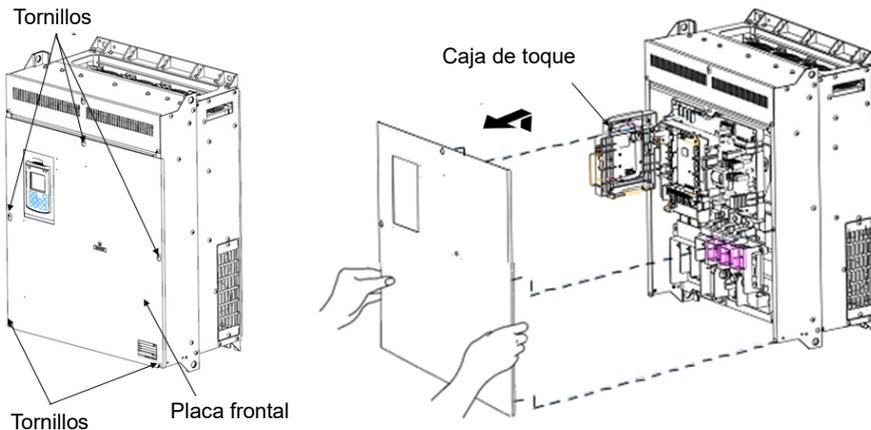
Extracción de la placa frontal y de la placa del cableado (FRN110AQ1S-4□)
